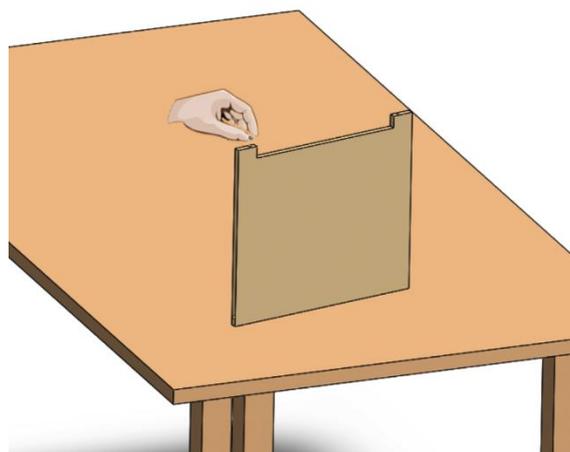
Paso 14 del ensamblaje del cajón (conjunto 2)
